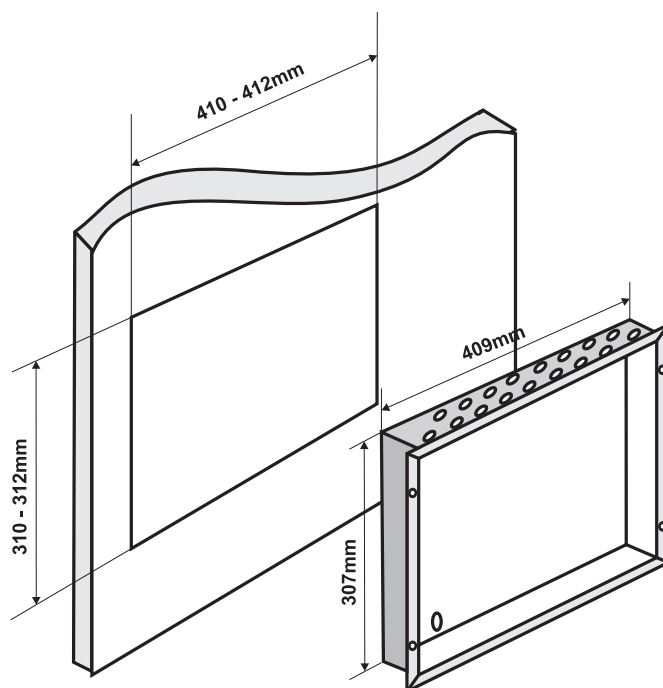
Dimensões da parte inferior de metal e orifício de montagem.
